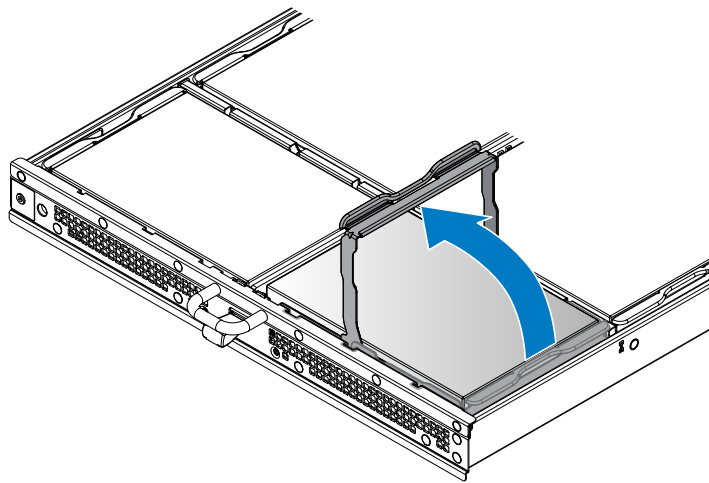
Déverrouillage de l'assemblage de disque dur 3,5 pouces
